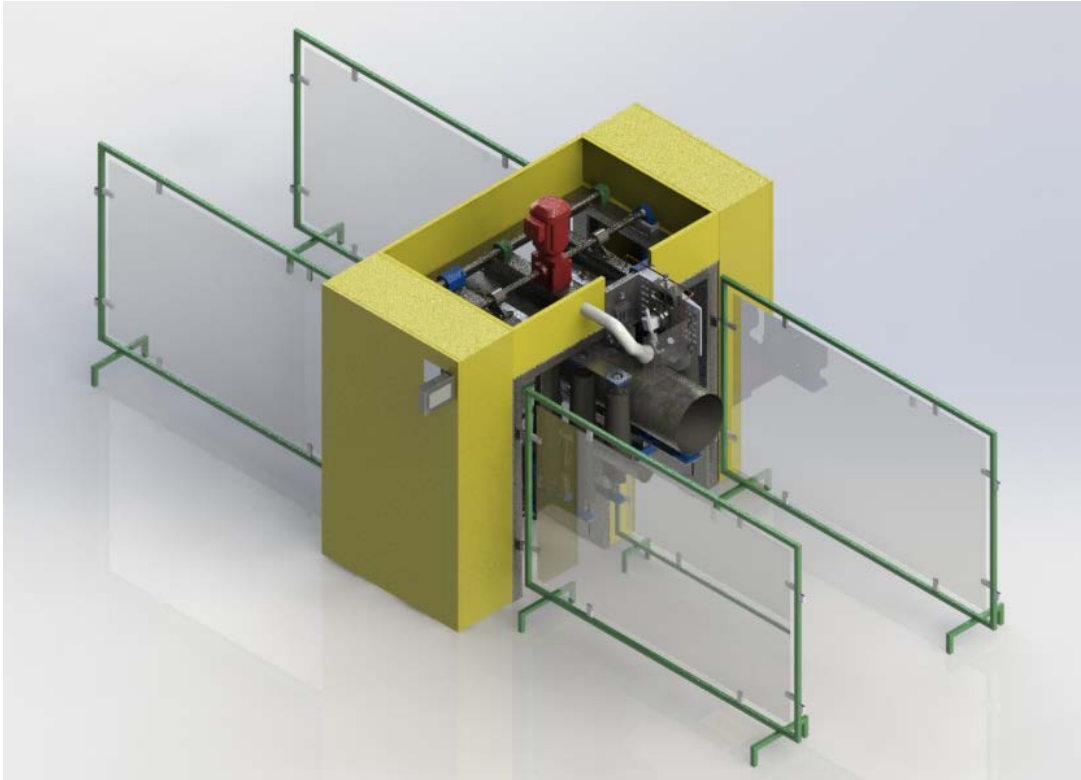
Equipamento de soldadura longitudinal de condutas.
